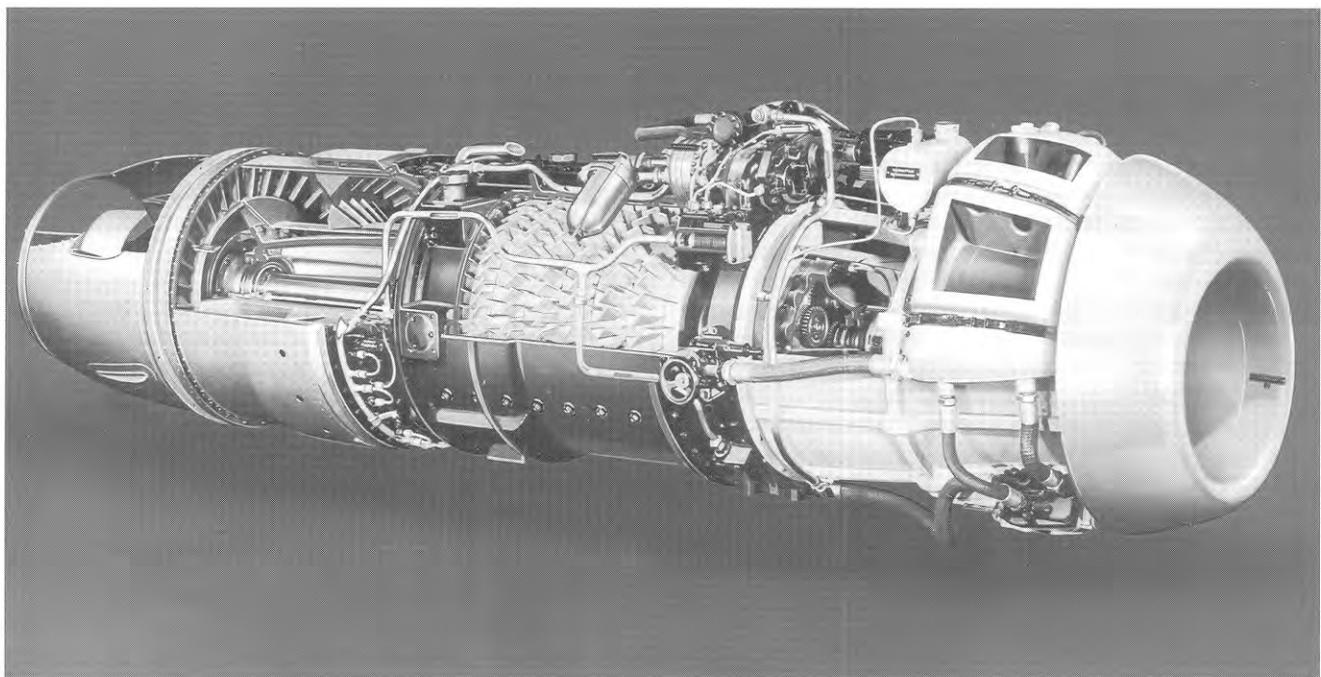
Турбореактивный двигатель БМВ 109-003 А
